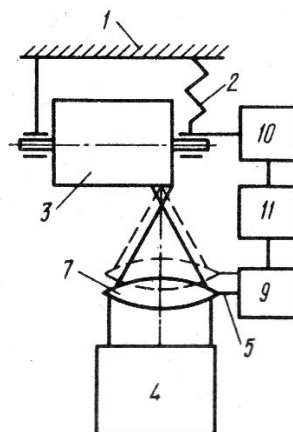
Схема лазерного устройства для балансировки роторов
